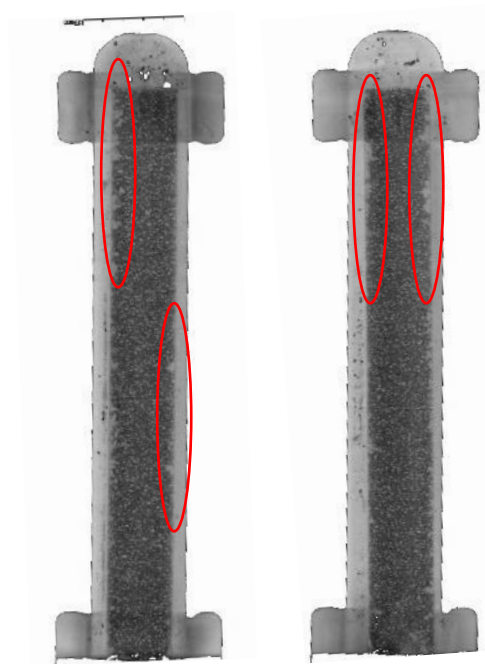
Hohler Salzkern im Druckgießwerkzeug auf der linken Seite, CT-Aufnahme des hohlen Salzkerns auf der rechten Seite
